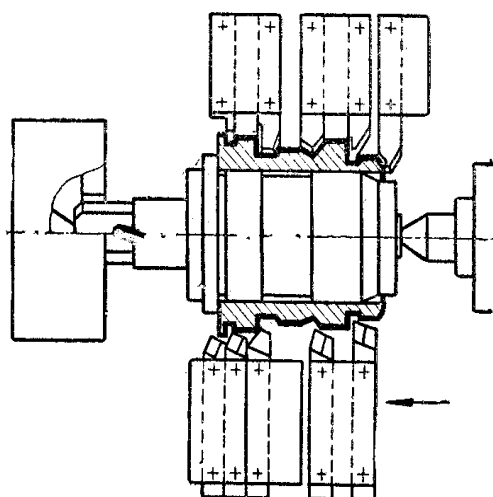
Схема обробки втулки із ступеневою зовнішньою поверхнею на багаторізцевому напівавтоматі
